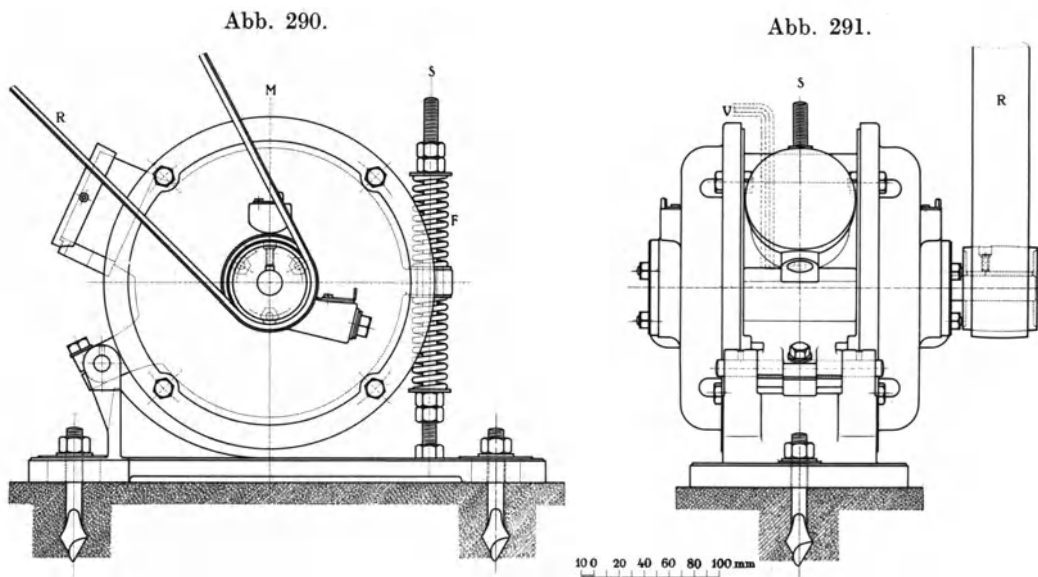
291. Gewöhnlicher Webstuhlmotor mit wippenartiger Motorlagerung.
